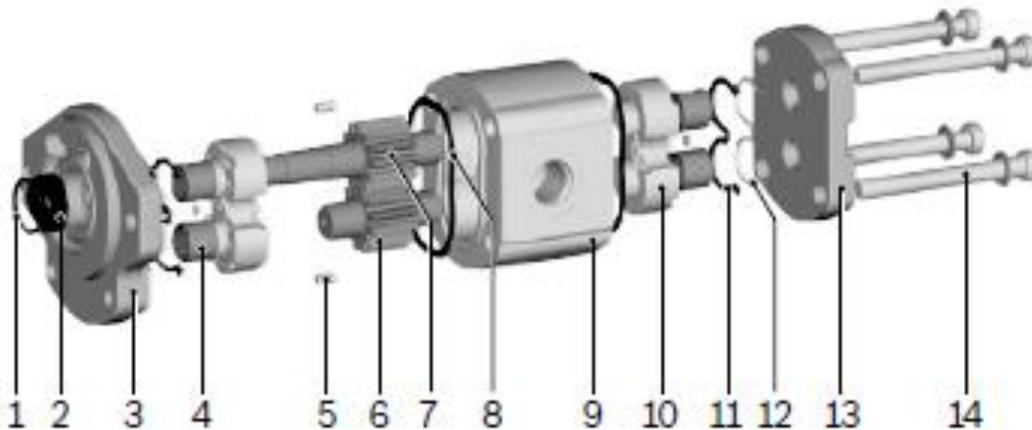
Componentes de bomba de engranajes con cuerpo de aluminio. [13]
